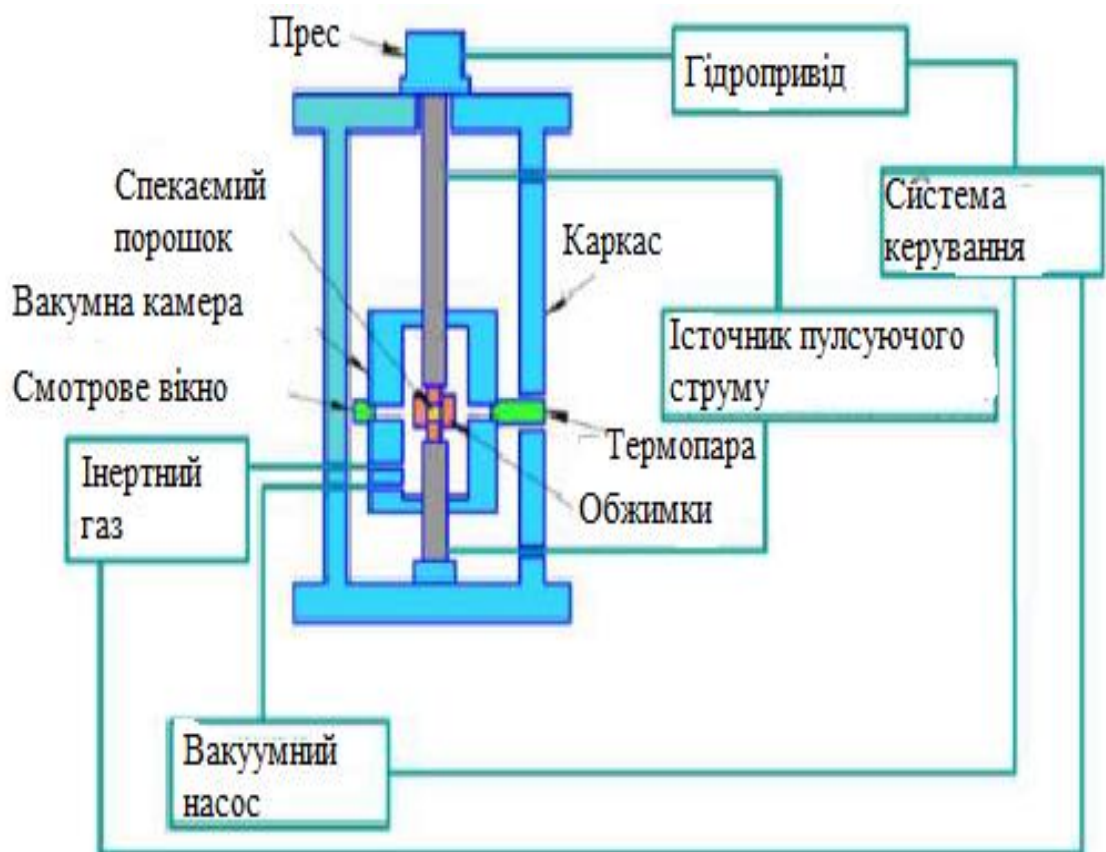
Принципова схема обладнання іскрового плазмового спікання [17].
